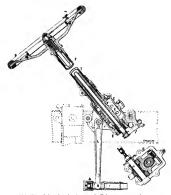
Schrauben-Lenkung mit Zahnstangenverzahnung.
